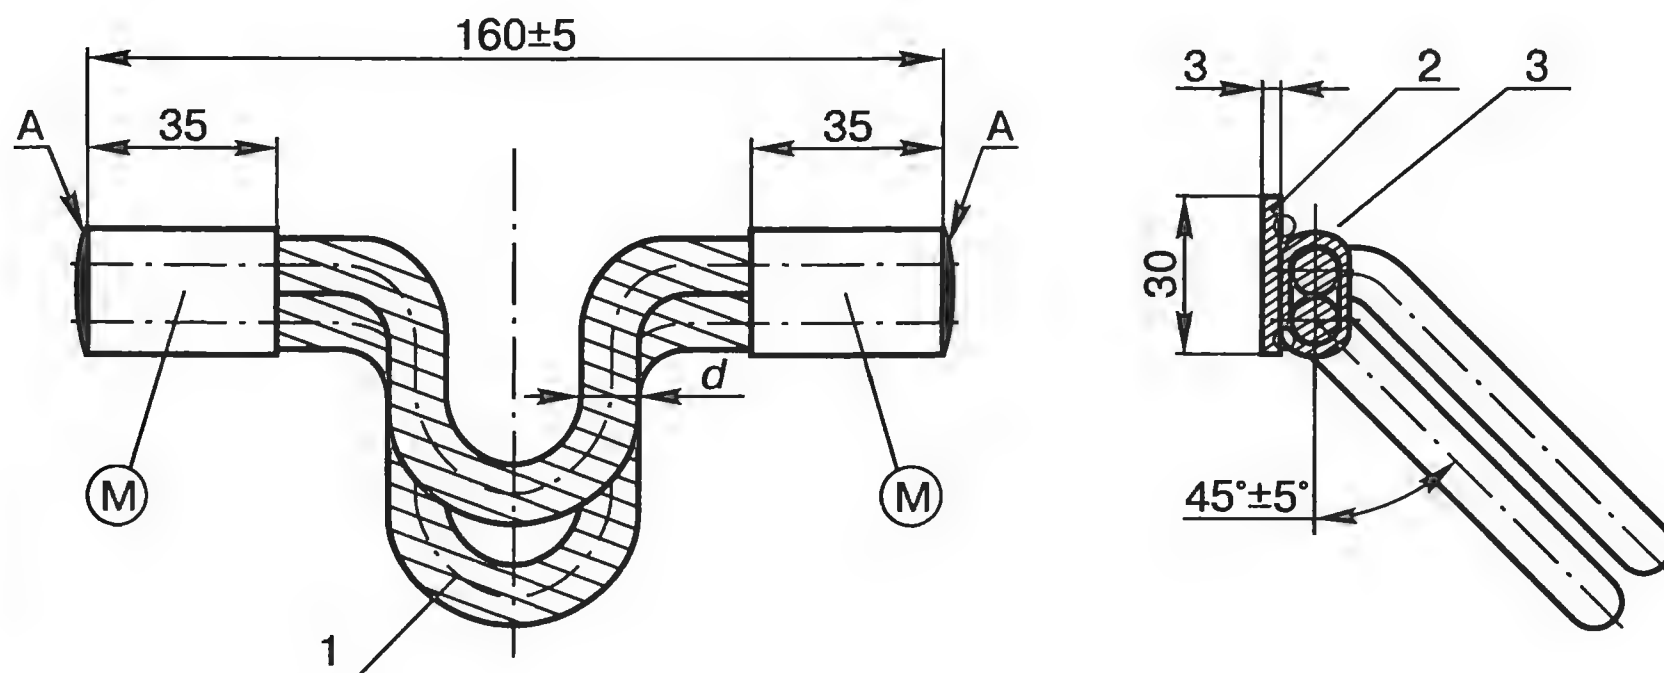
Соединители стыковые приварные фартучные сталеаледные СПСМ
